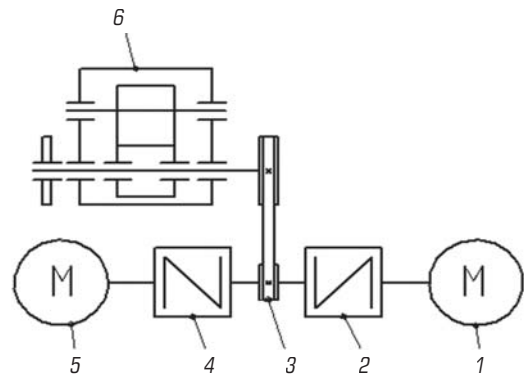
Кинематическая схема привода щековой дробилки до модернизации:
